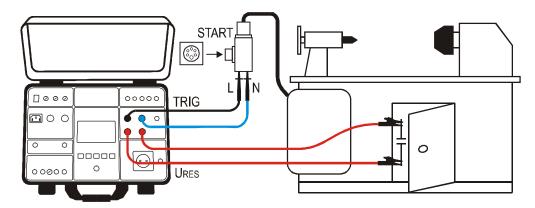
Ligação das ponteiras de teste para medição URES INT em máquinas ligadas 1P/3P
